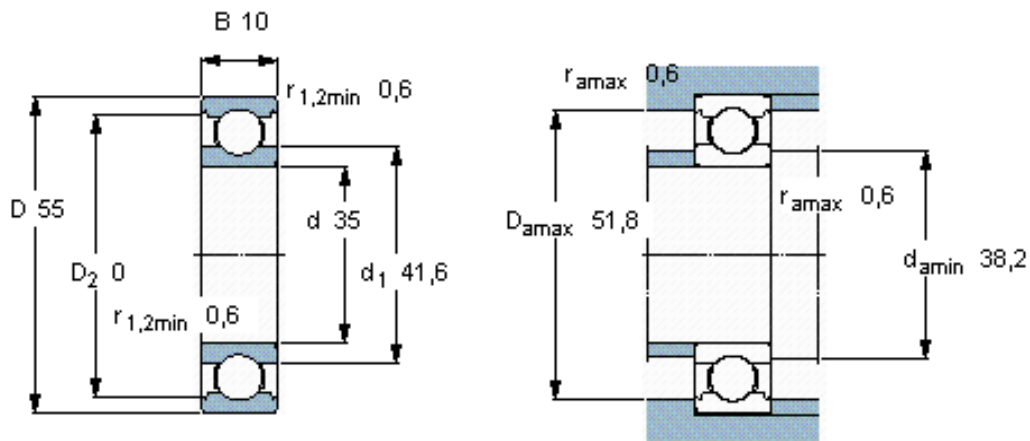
Dimensiones del Rodamiento SKF 61907.
